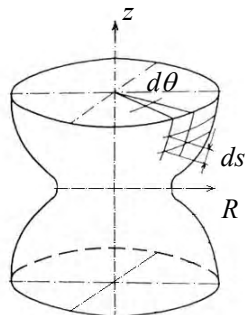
Схема разбиения заготовки на участки в цилиндрической системе координат
